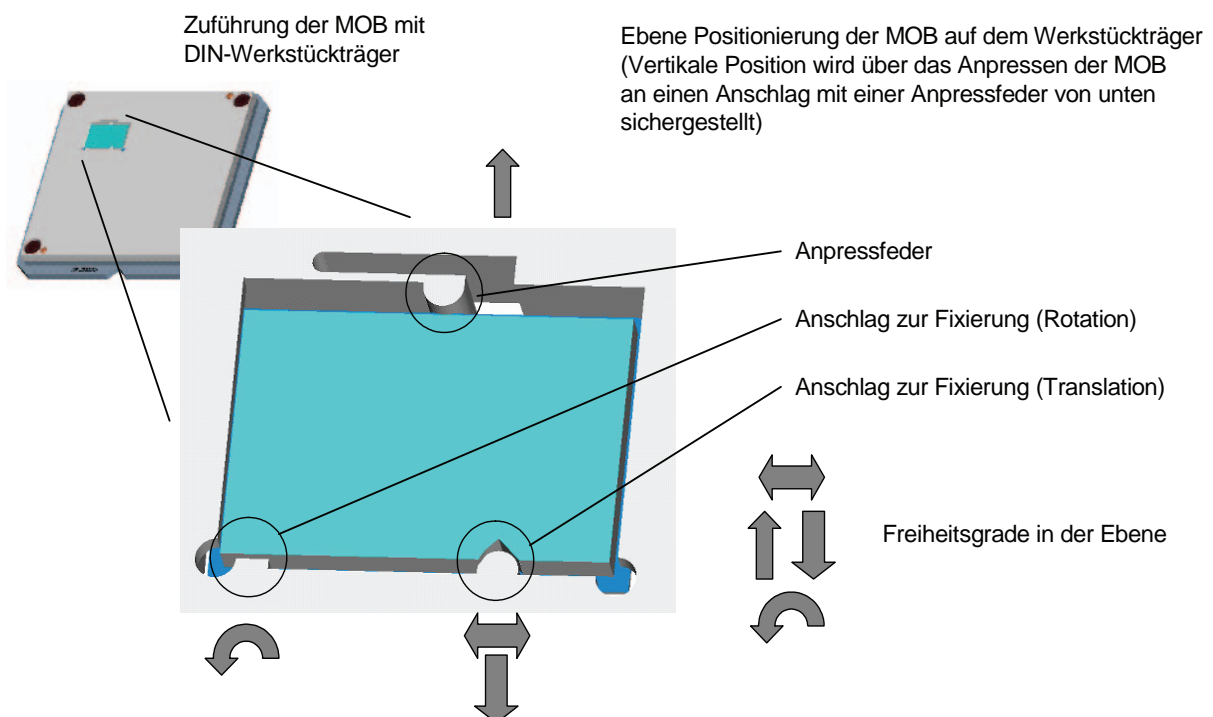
Positionierung der MOB auf Werkstückträger über passive Anschläge und Federn
